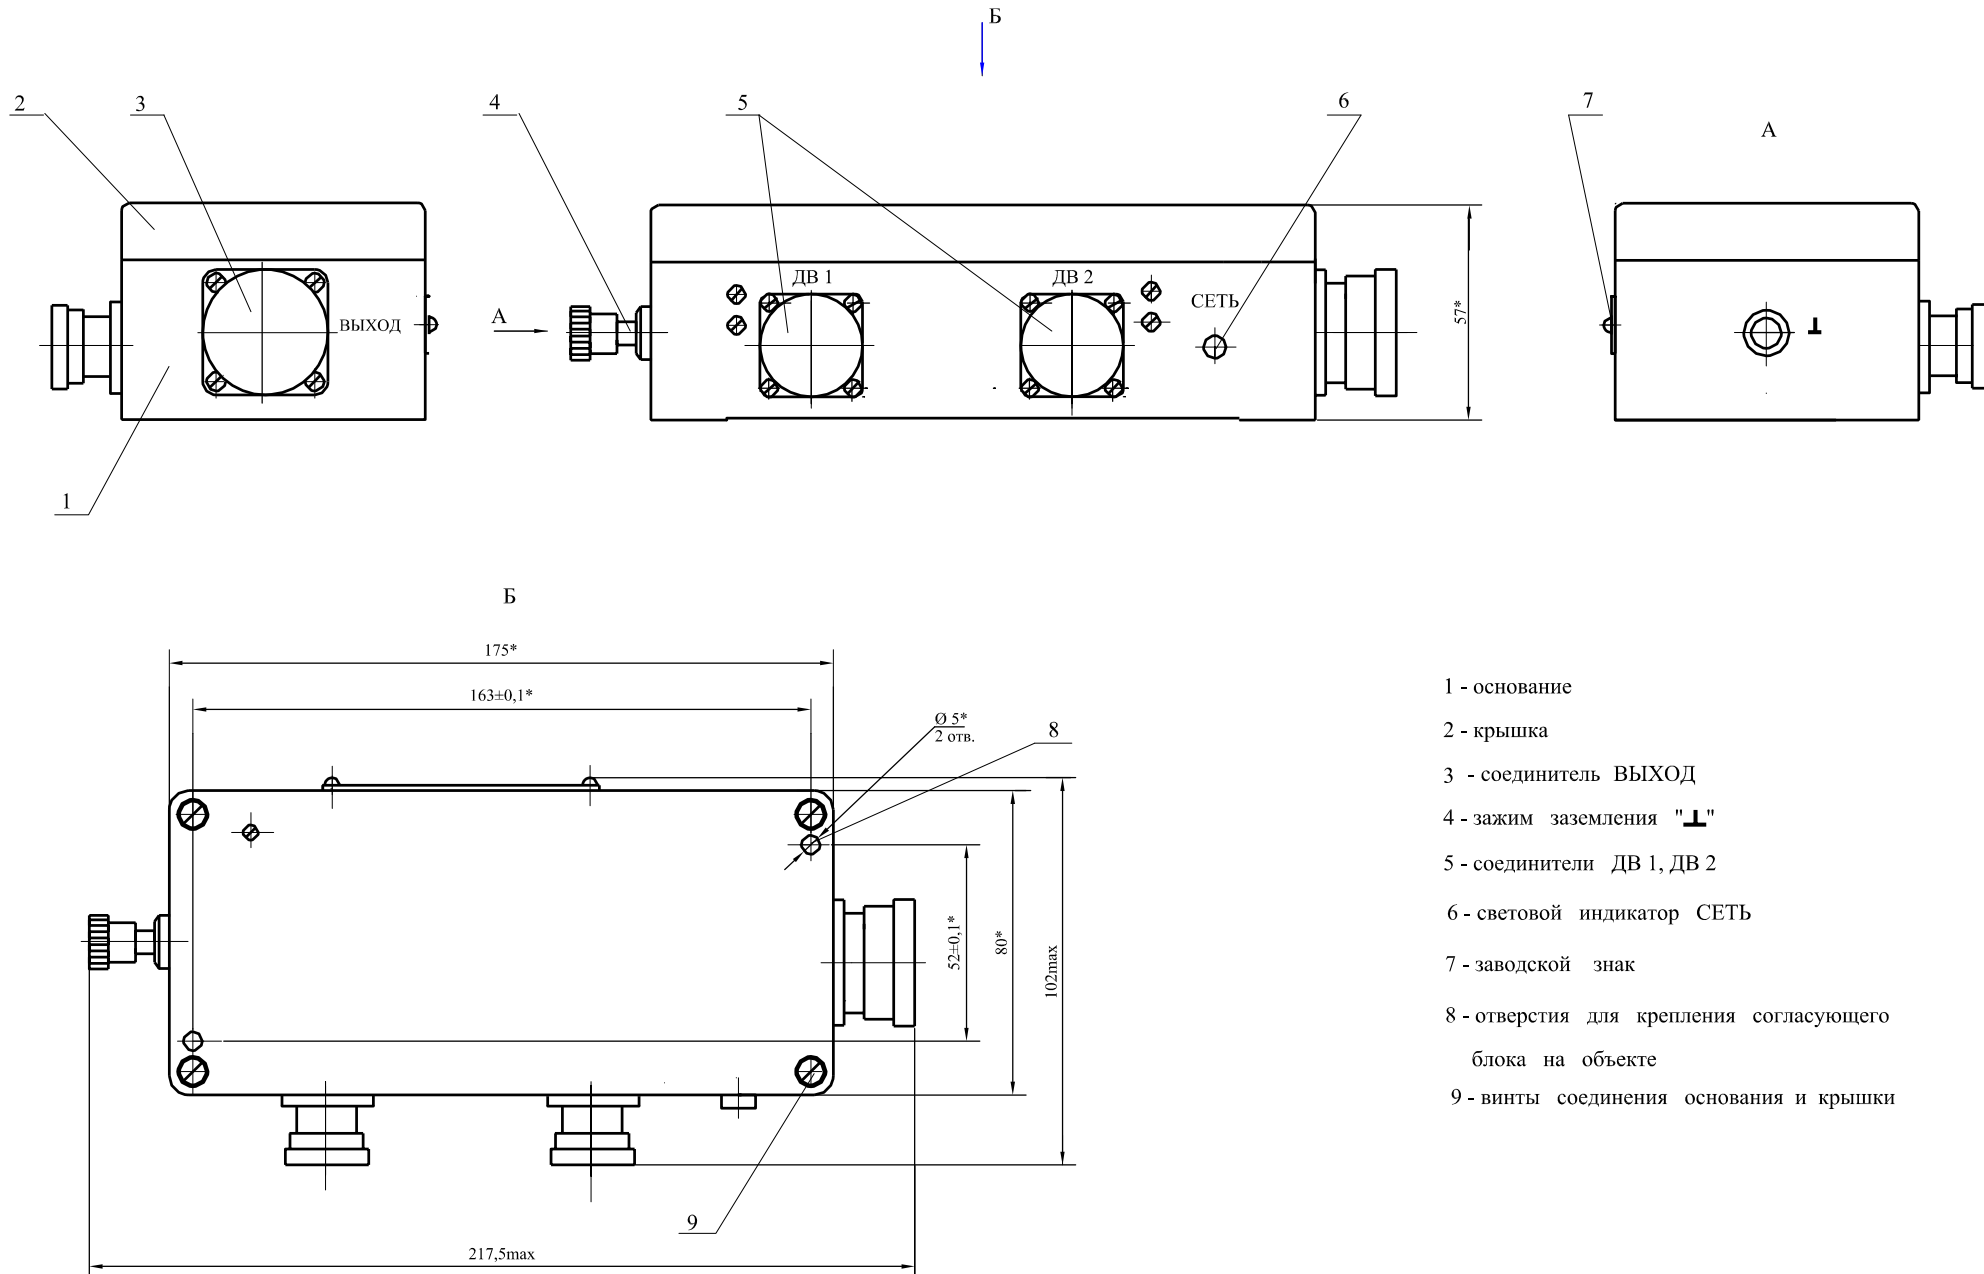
Габаритно-установочные размеры согласующего блока
